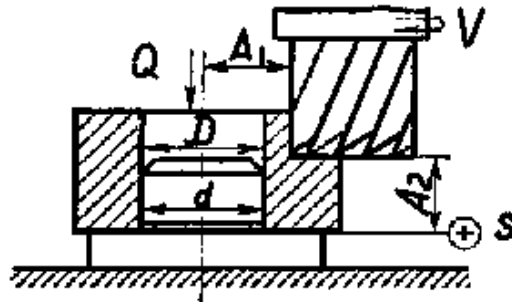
Схема фрезерования втулки (к задаче 11)
